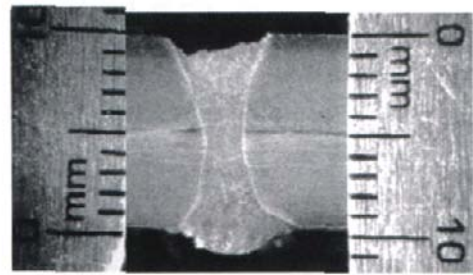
匙孔模式下双面PAW+TIG工艺焊缝形貌
